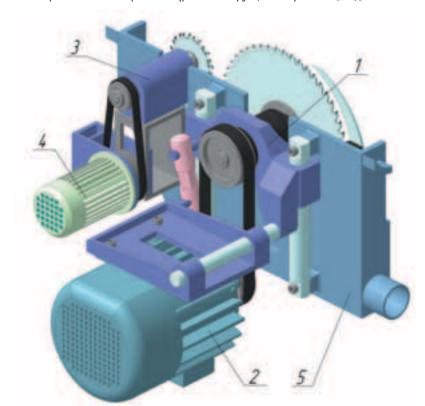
Устройство пильного блока: 1 — блок основной пилы; 2 — привод основной пилы; 3 — блок подрезной пилы; 4 — привод подрезной пилы; 5 — корпус
